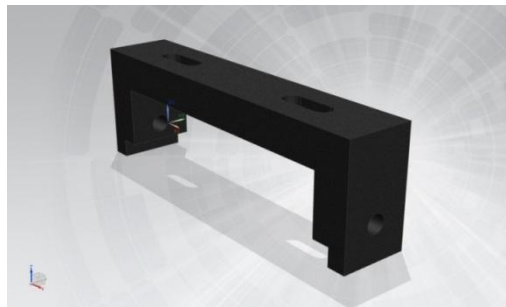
Soporte tipo corredera diseñado para la unidad de rodamientos seleccionada.
